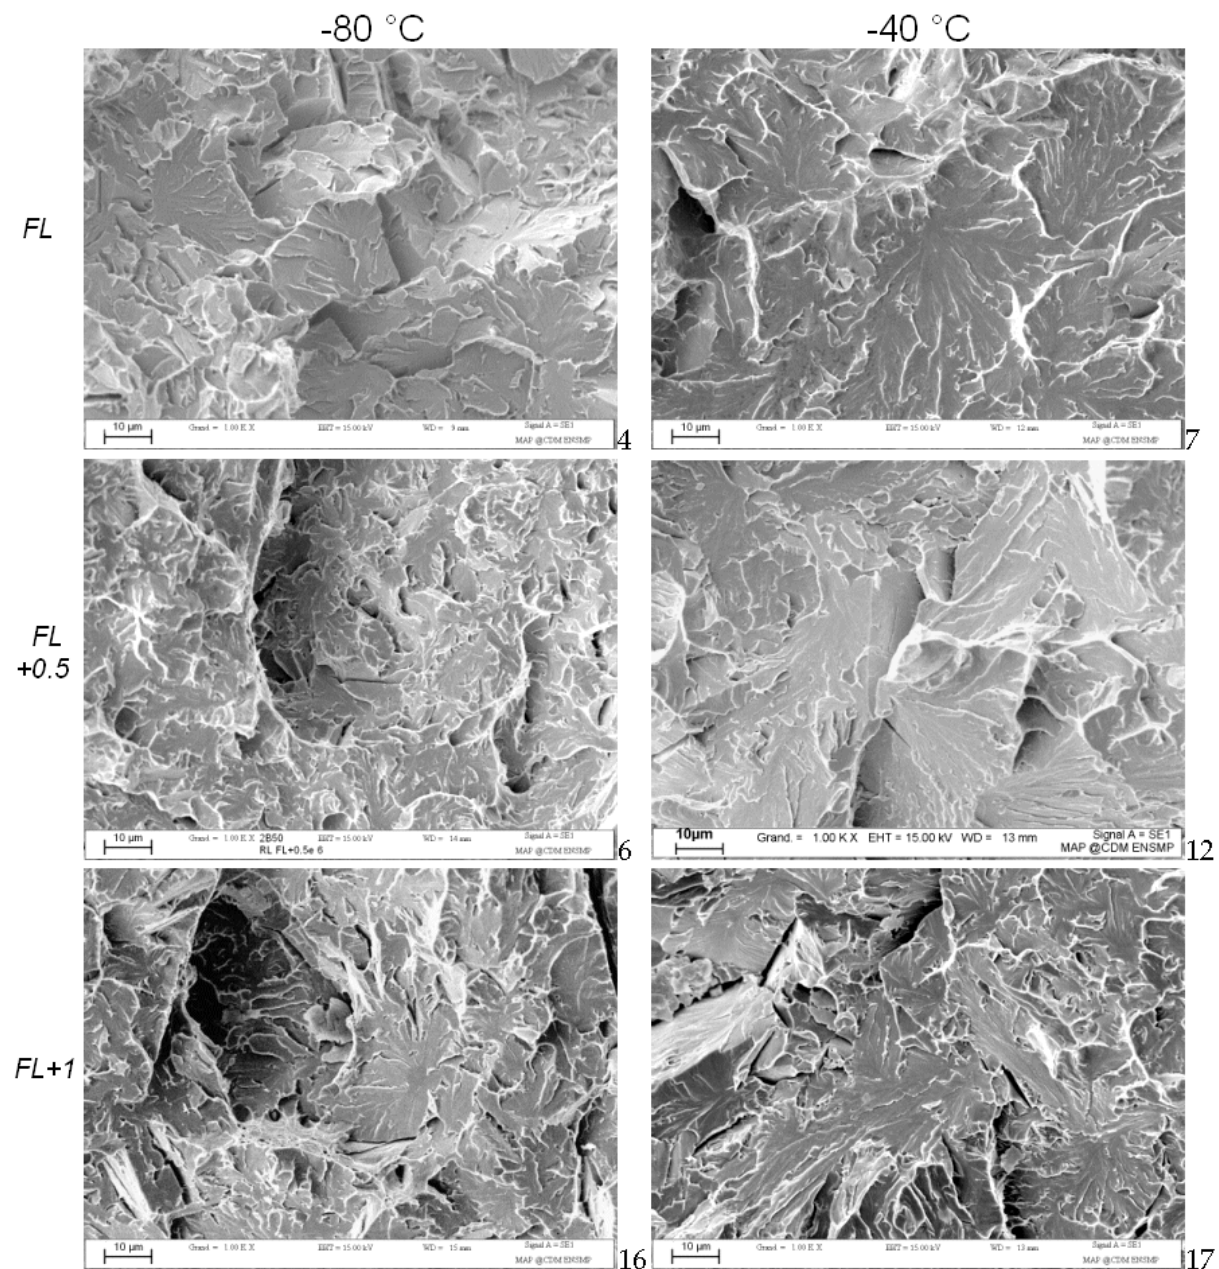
Fractographies dans le plan TS des éprouvettes Charpy 2B50 entaillées en FL+x
